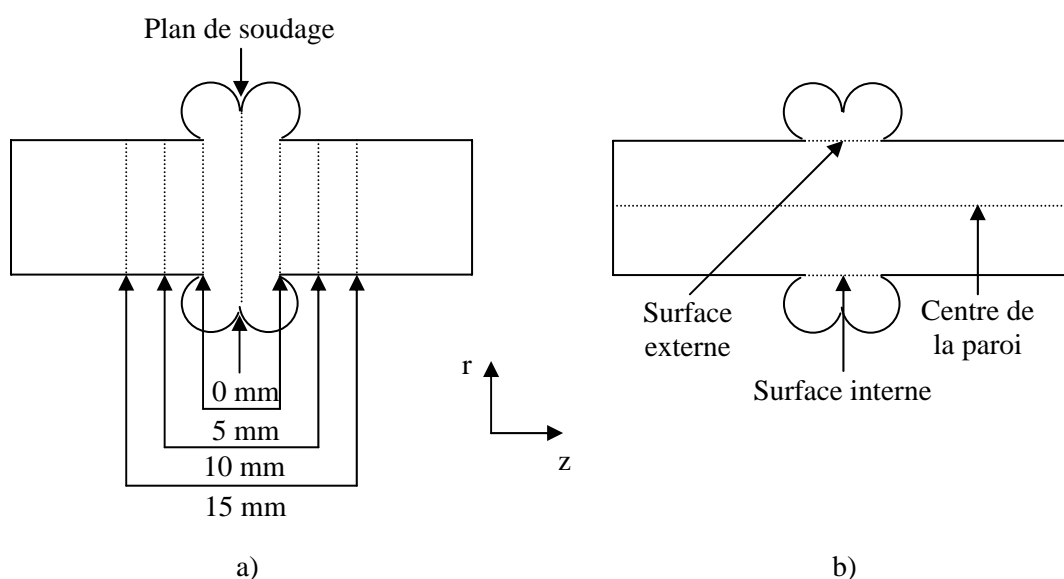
Schéma des plans de prélèvement des échantillons. a) dans les plans parallèles au plan de soudage (plans $r\theta$) ; b) dans les plans perpendiculaires au plan de soudage (plans θz)
